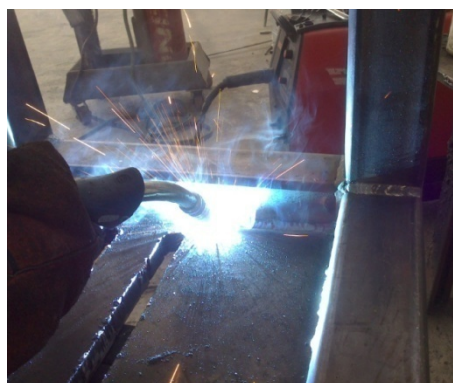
Soldadura de las planchas de la mesa
